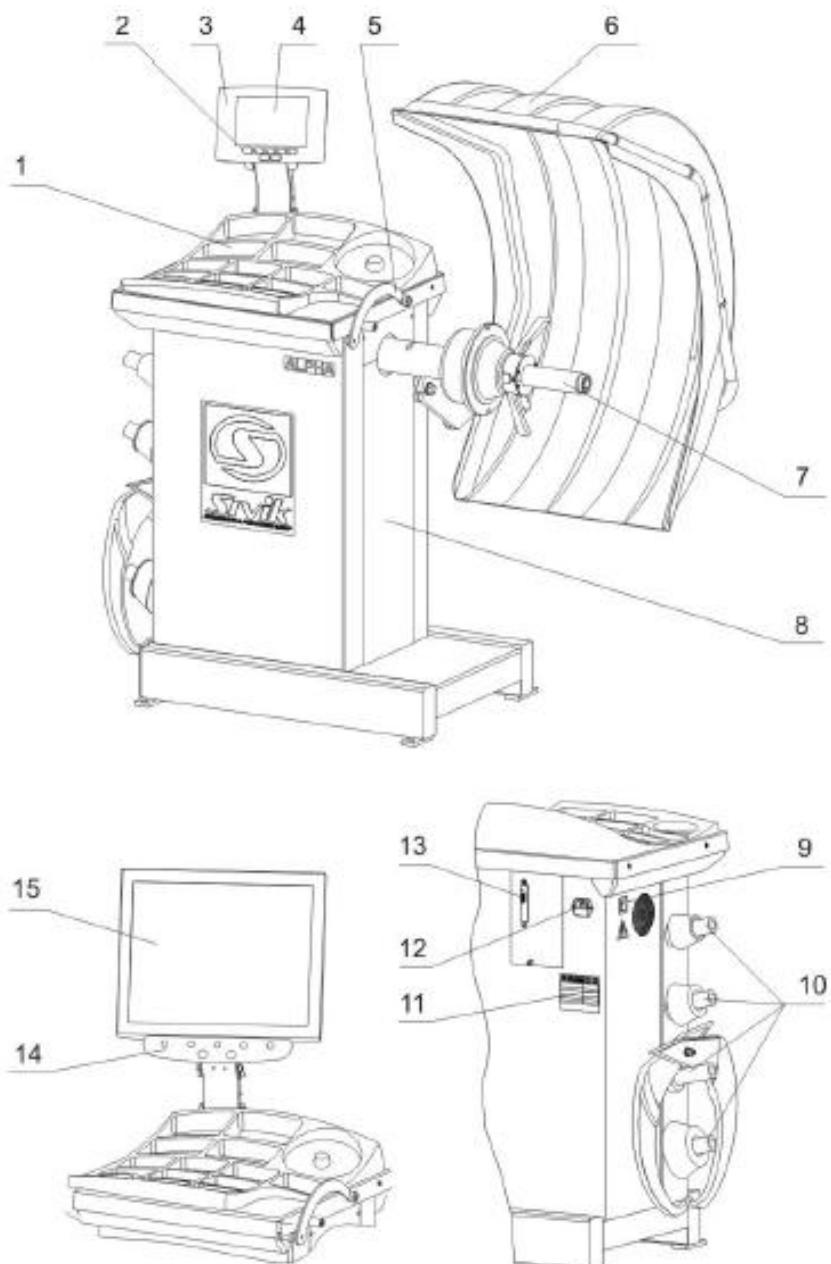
Устройство стенда Sivik Alpha 1 - панель пластмассовая; 2 - клавиатура; 3 - пульт управления; 4 - дисплей; 5 -линейка электронная; 6 - кожух защитный; 7 - вал; 8 - корпус; 9 - выключатель сетевой; 10 - пальцы для размещения конусов и кронциркуля; 11 - шильда; 12 -вилка сетевая с предохранителем для подключения сетевого шнура; 13 - гнездо для подключения DVI кабеля монитора; 14 - клавиатура; 15 - монитор.
